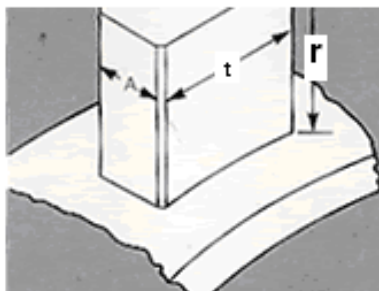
Dimensiones de una Escobilla, tomado de [19]
